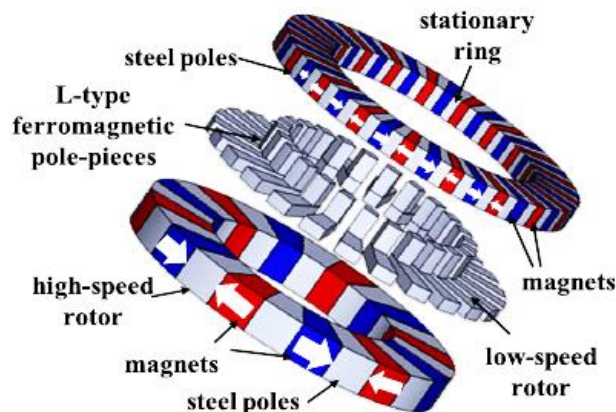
Engrenage magnétique à pièces ferromagnétiques en forme de L [TSA15].
